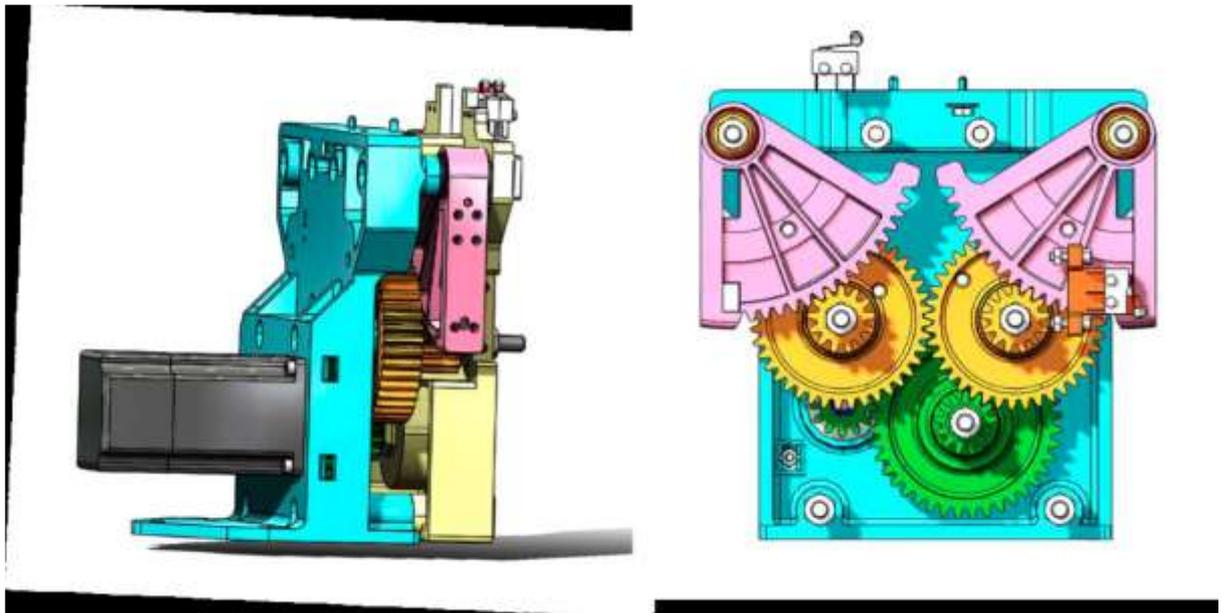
Mecanismo actuador PA12. Fuente: Galindo i Anquera, Preguntas Frecuentes, 2021.
